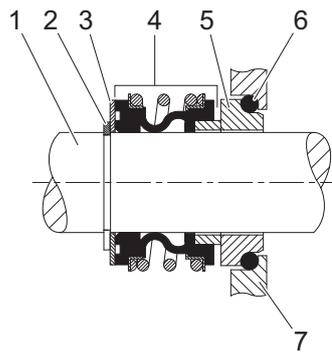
Aufbau Gleitringdichtung mit Elastomerbalg und mit O-Ring
